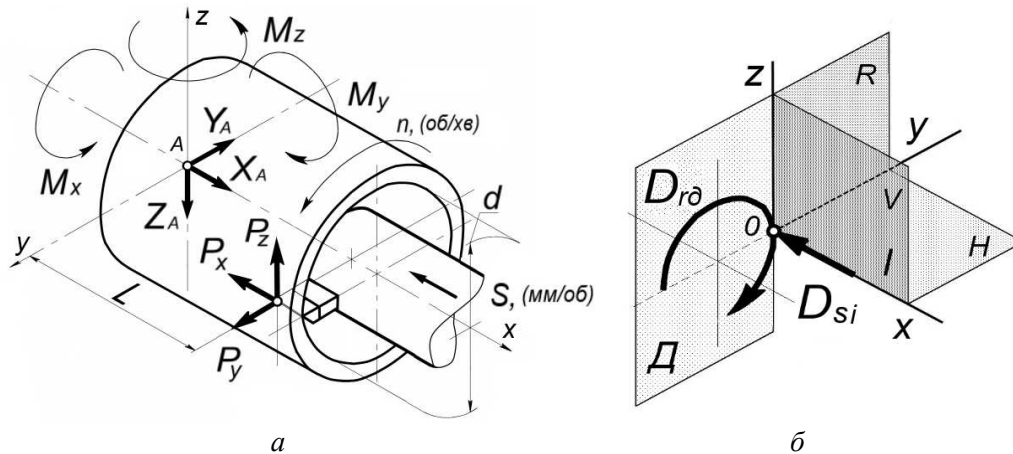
Схеми розточування отвору: а – розрахункова схема розточування отвору на верстаті токарної групи; б – принципова кінематична схема розточування отвору
